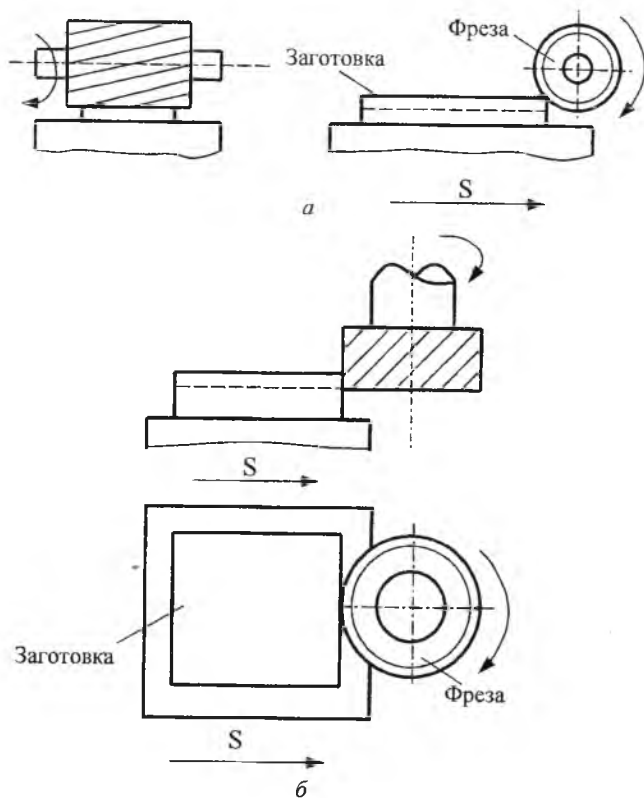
Схема фрезерования: а – цилиндрическое; б – торцевое
